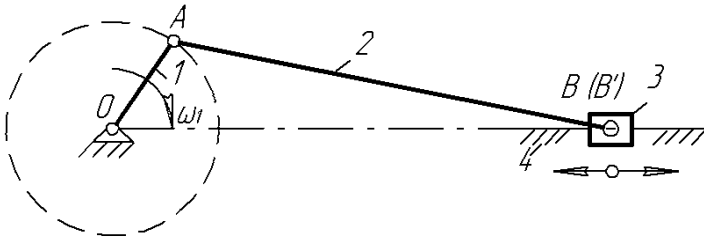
Кінематична схема кривошипно-повзунковий механізм
